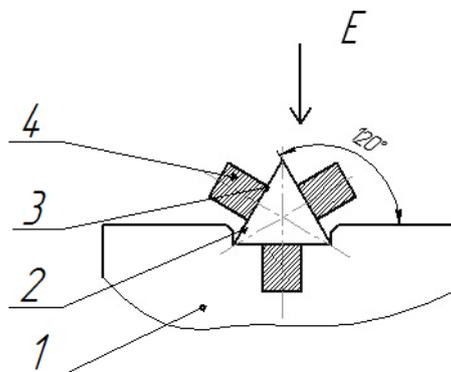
Схема сварки трубки и ребра стержня;
